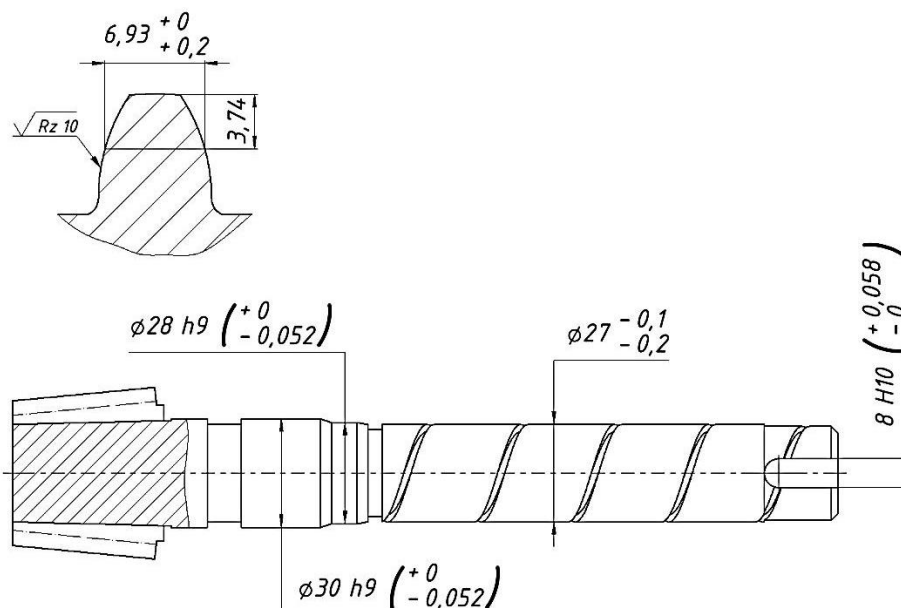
рабочий чертеж вала-шестерни С.КР 700-00-22
